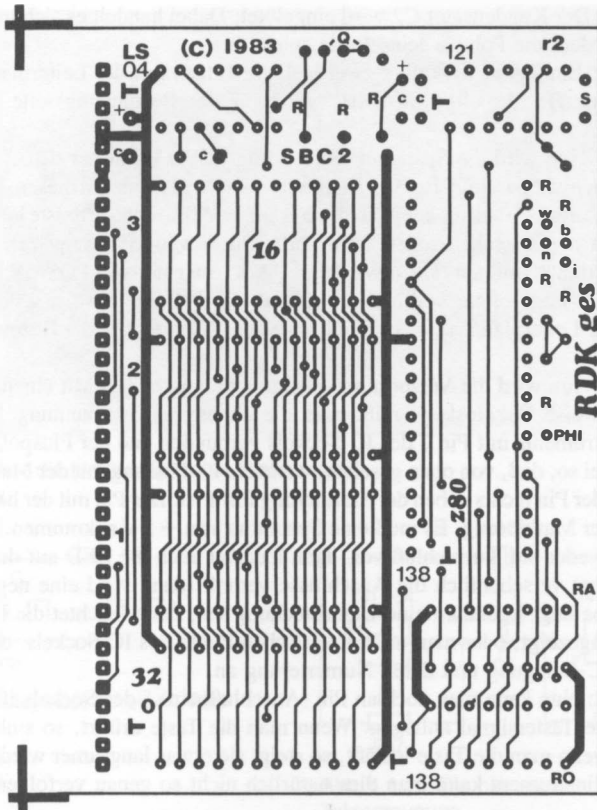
Die Bestückungsseite der Baugruppe SBC 2
